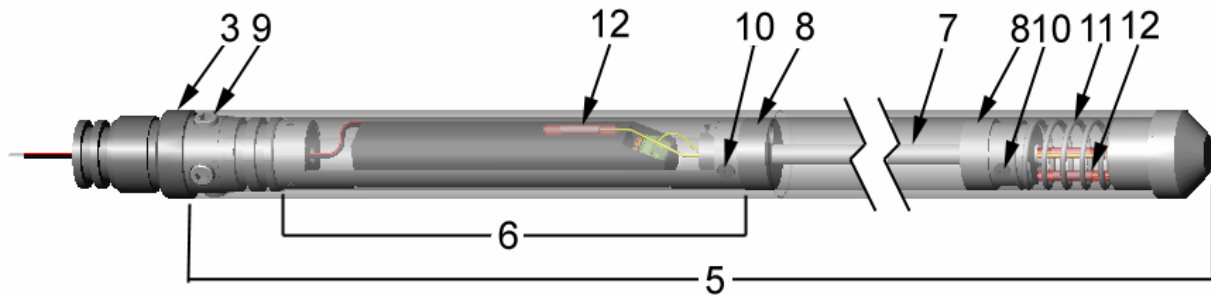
Assemblage de l'outil de séparation pour masse-tige
